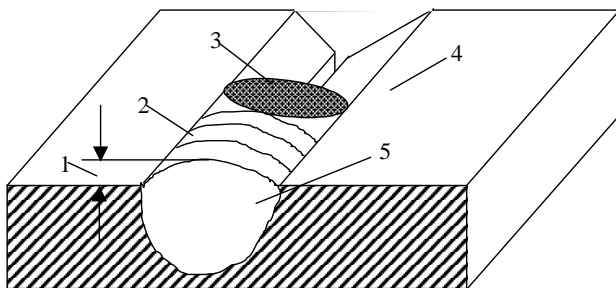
Сварной шов: 1 – усиление шва; 2 – сварной шов; 3 – сварочная ванна; 4 – основной металл; 5 – металл шва
